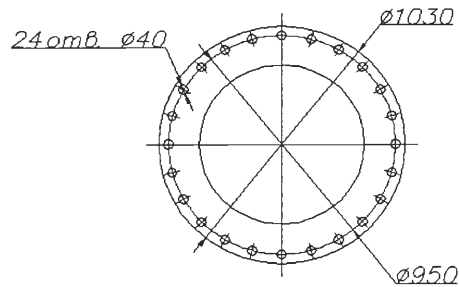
Фланцевые соединения для установки на фундамент композитных опор ПКФ 110-1, ПКФ 110-2.
